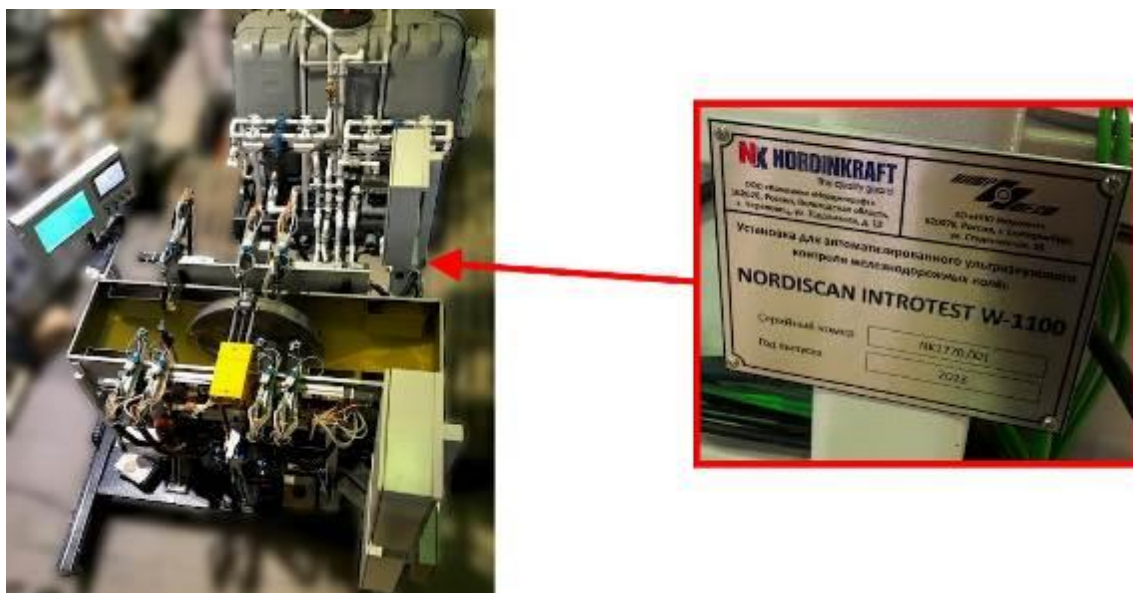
Общий вид и место нанесения заводского номера установок
